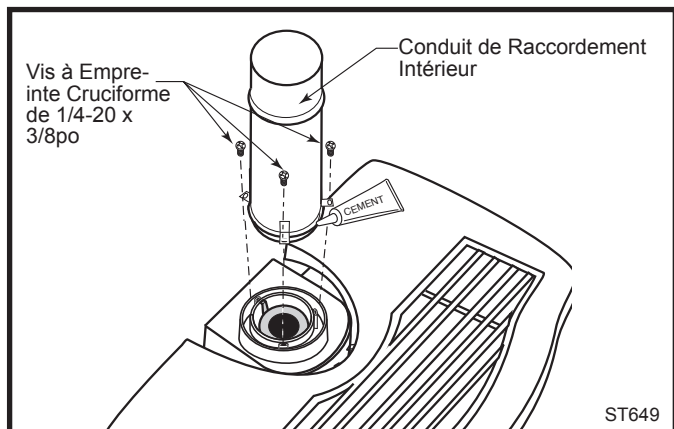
Installation du conduit de raccordement intérieur DuraVent.
